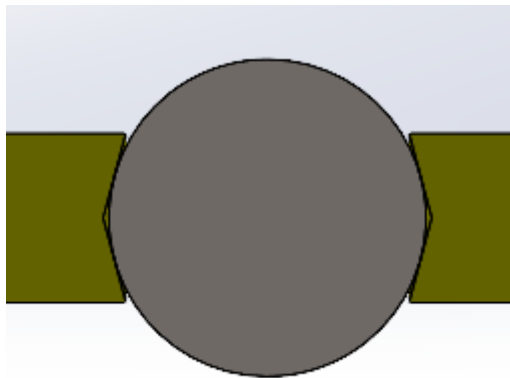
Vista in sezione: particolare della compressione delle boccole sulla sfera
